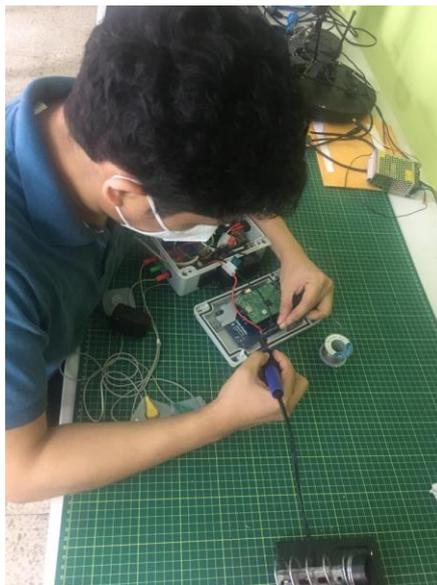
Soldadura del prototipo de telemedicina
